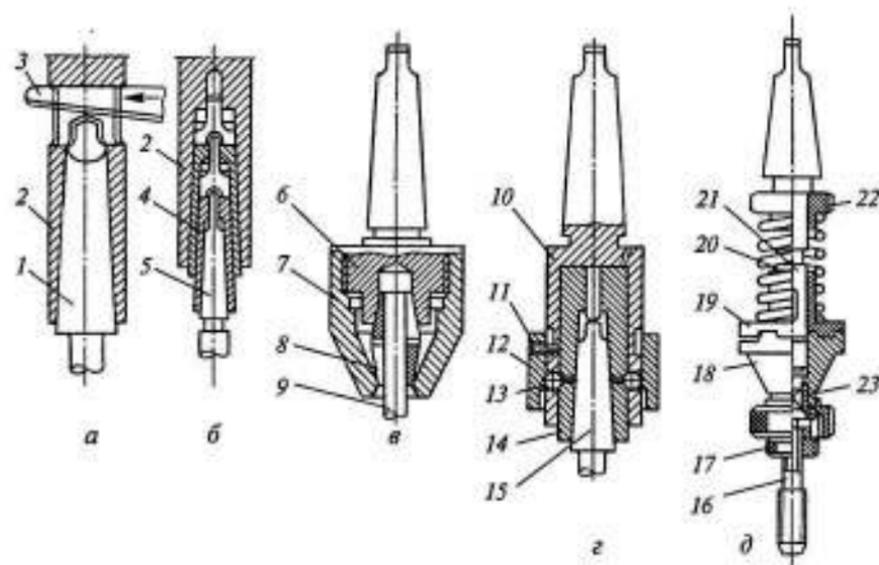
Устройства для закрепления осевого инструмента на сверлильных станках:
